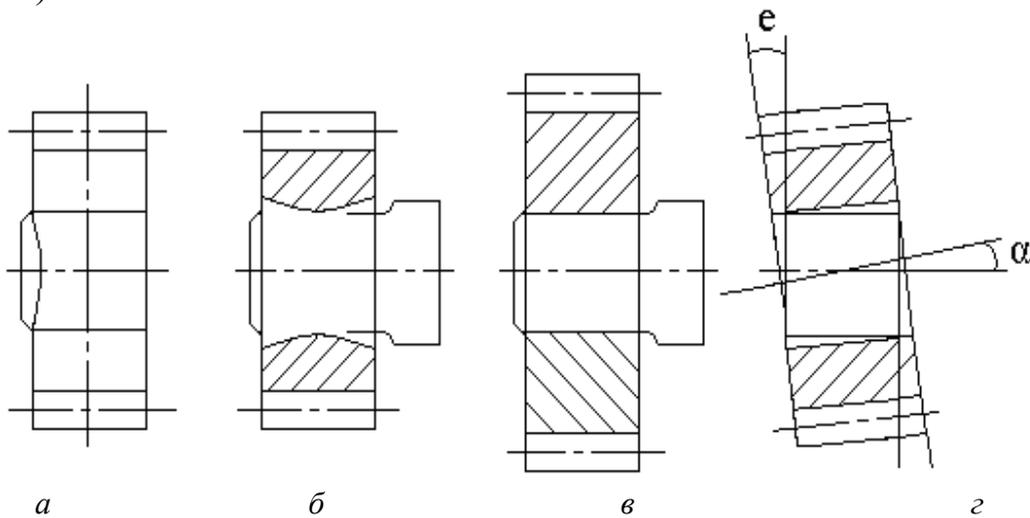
Погрешности при напрессовке цилиндрического зубчатого колеса
